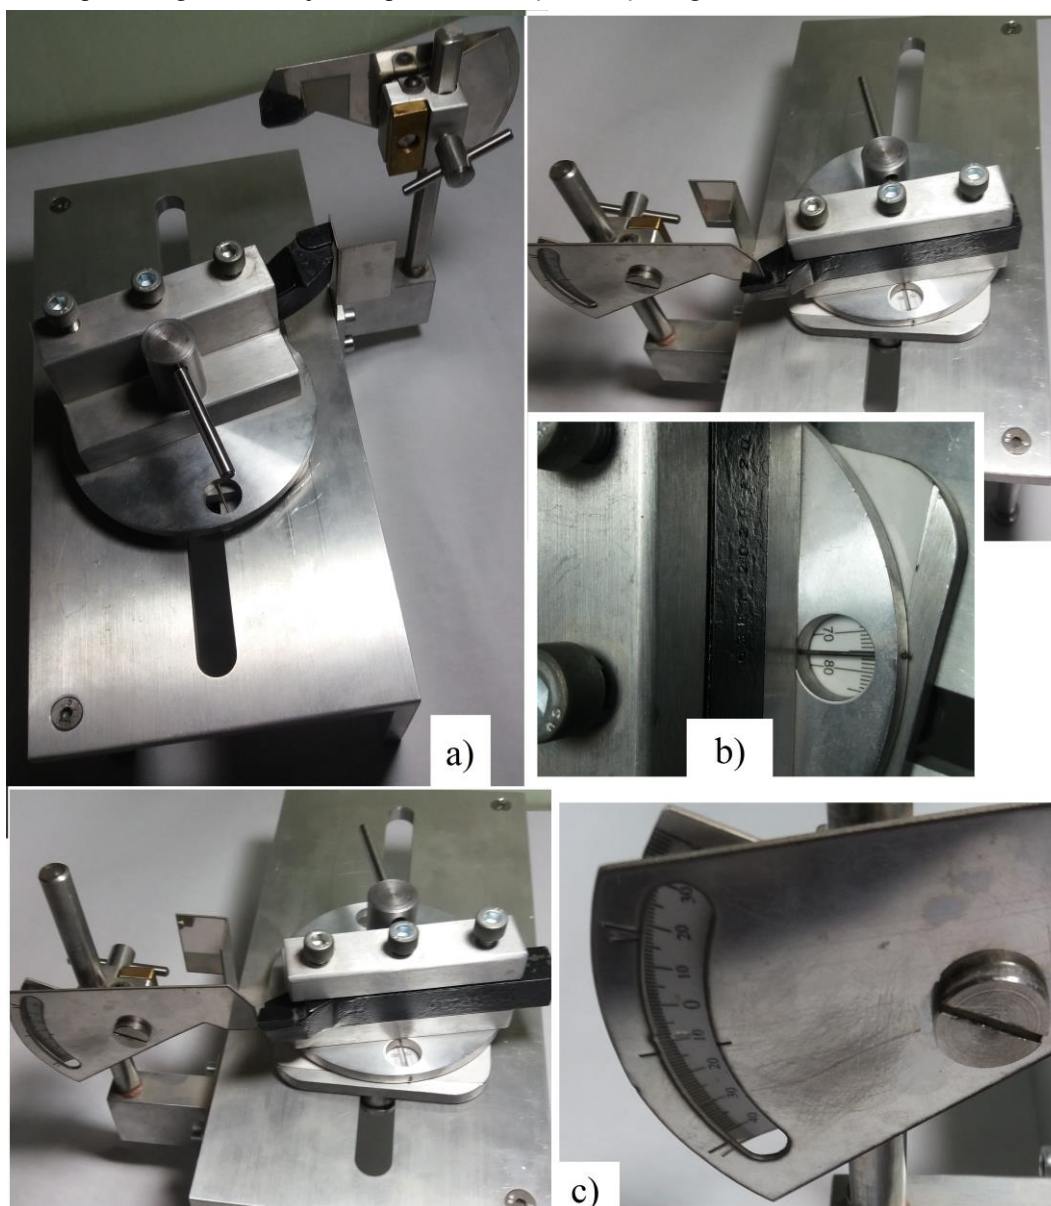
Măsurarea unghiurilor secundare ale cuțitului de strung
